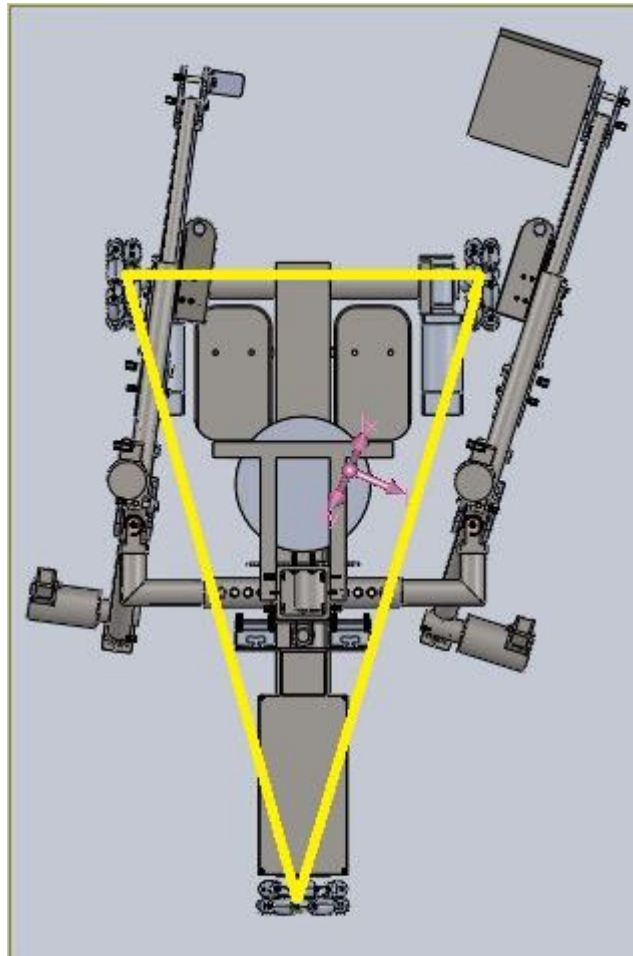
Planta del conjunto de exoesqueleto con centro de gravedad indicado. Fuente propia.
